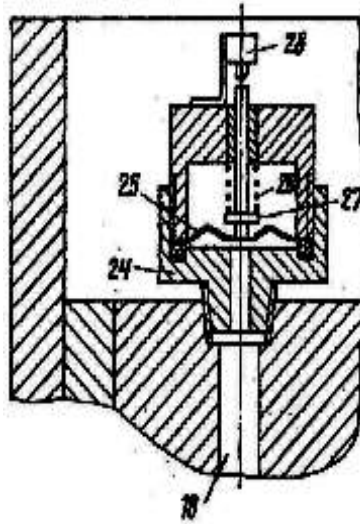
Розріз Б-Б вакуумної присоски
